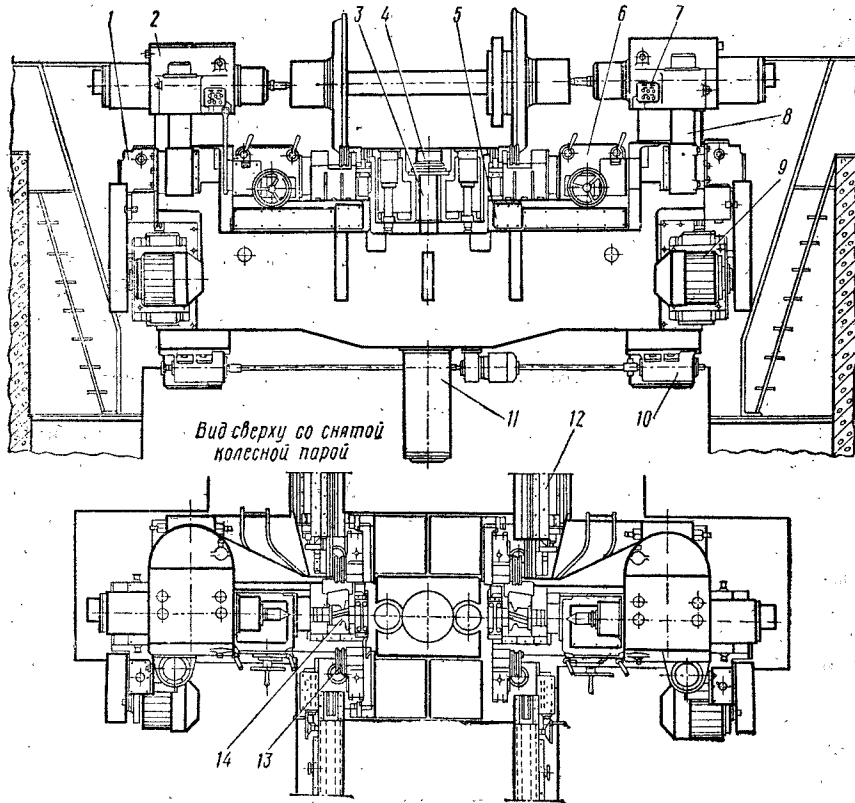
Фрезерный станок КЖ-20 для обточки бандажей колесных пар без выкатки
